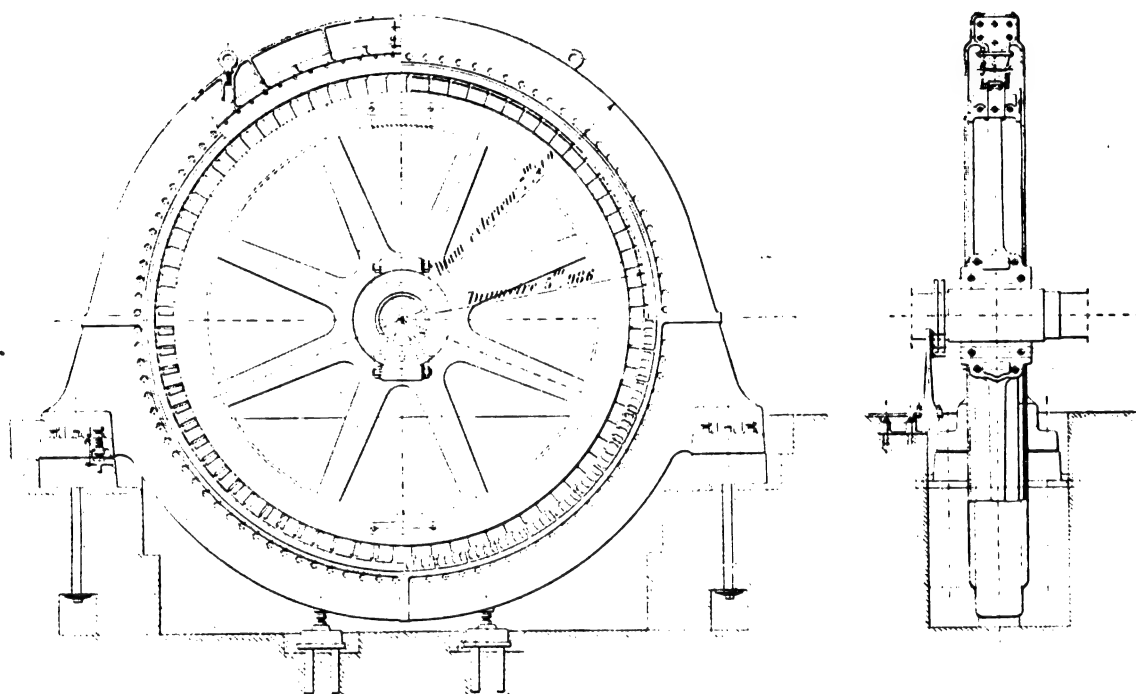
et 3. — Vue d'ensemble et coupes partielles de l'alternateur de la Compagnie de Fives-Lille.
